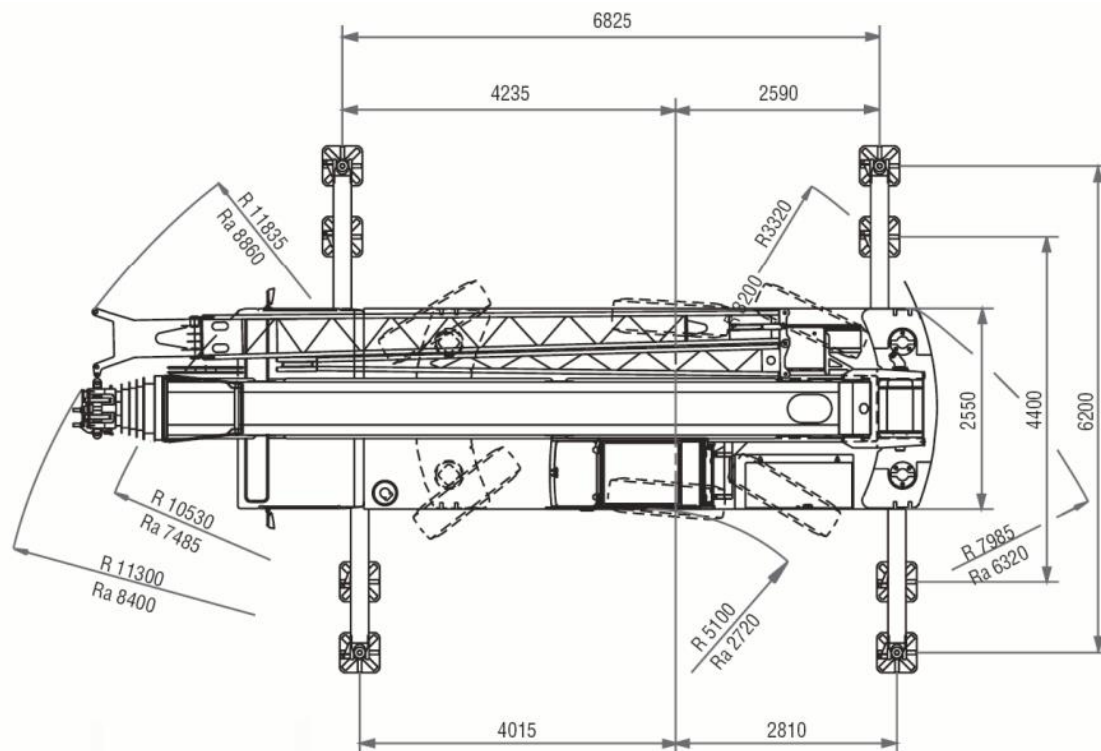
Zátěžový diagram mobilního jeřábu
